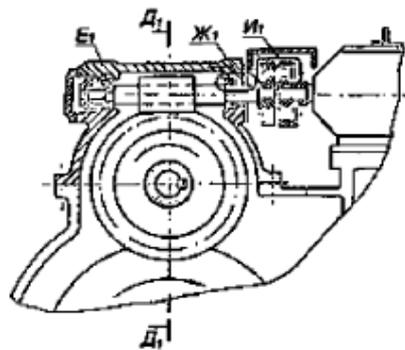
Поперечный разрез валоповоротного устройства турбины ПТ-80/100-130/13 ЛМЗ [3]
